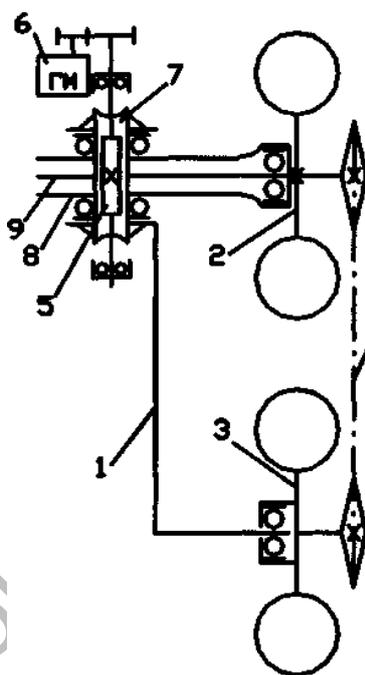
Кинематическая схема разработанной бортовой поворотной передачи: 1 – поворотное плечо; 2, 3 – колеса; 4 – цепная передача; 5 – червяк; 6 – гидромотор; 7 – червячное колесо; 8 – кожух ведущего моста; 9 – полуось
